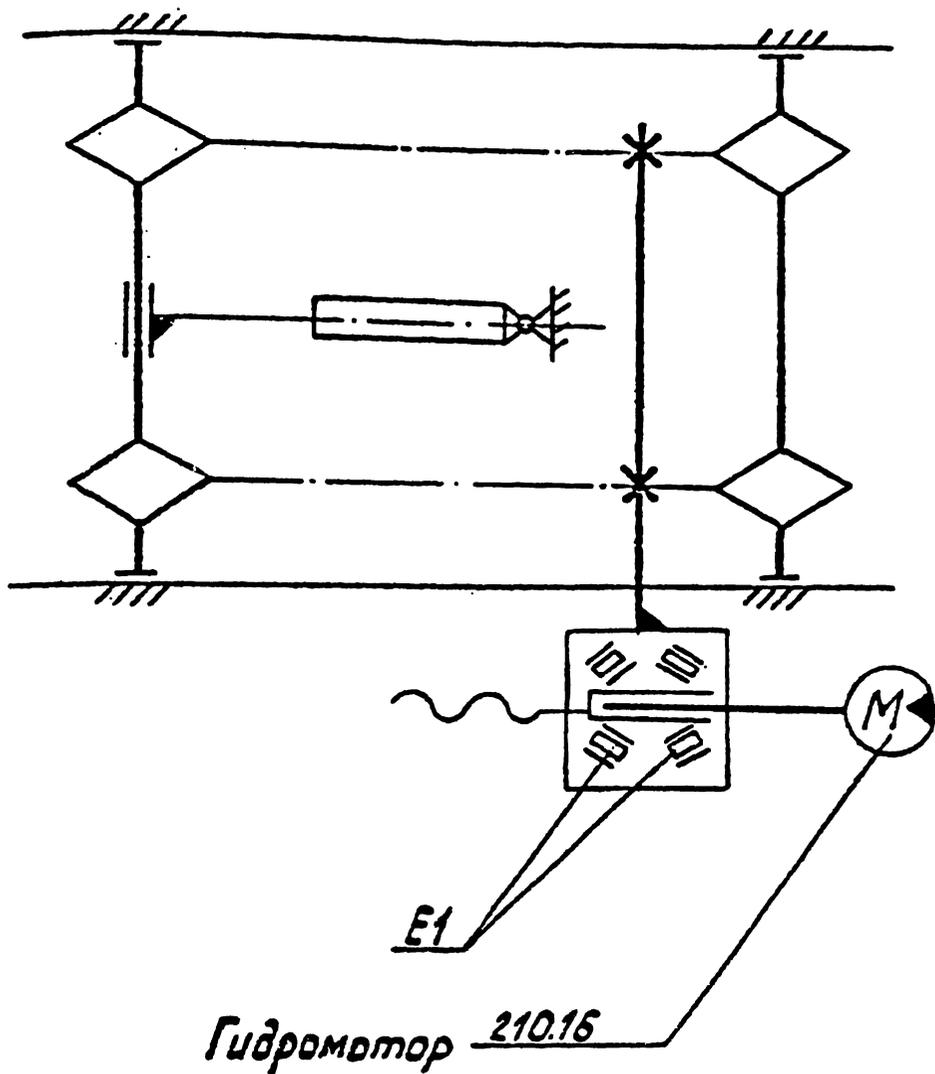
Кинематическая схема буровой каретки комбайна «Урал-20А» E1 - подшипники
